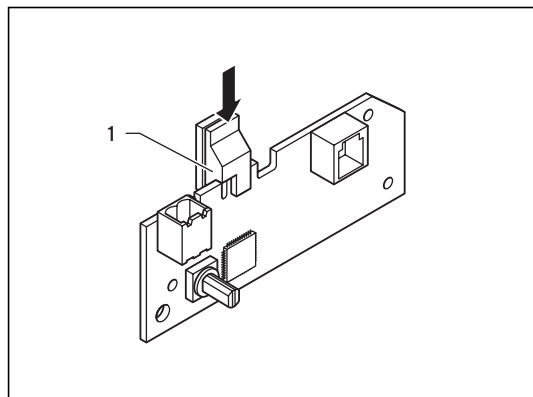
Montaje de la placa del acoplador de bus
